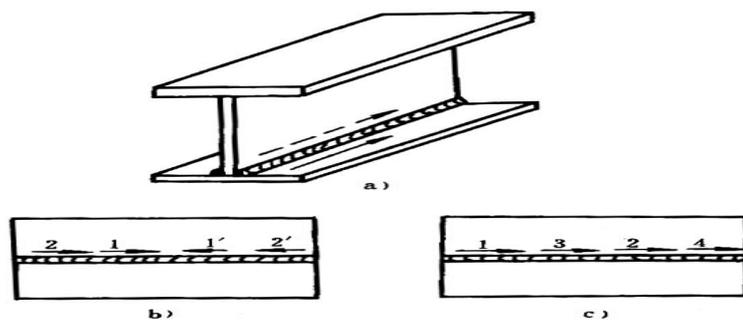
a) 长焊缝同方向焊接 b) 逆向分段退焊法 c) 跳焊法
